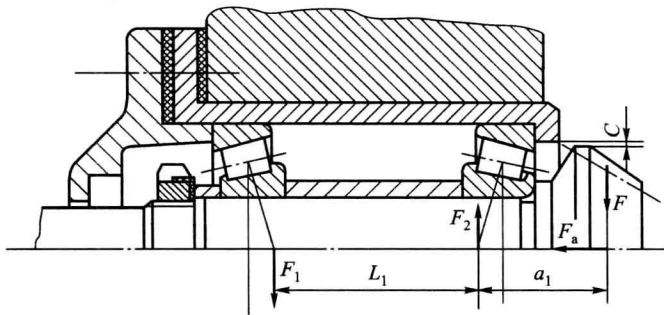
21 采用角接触向心轴承轴组件的两端固定结构
